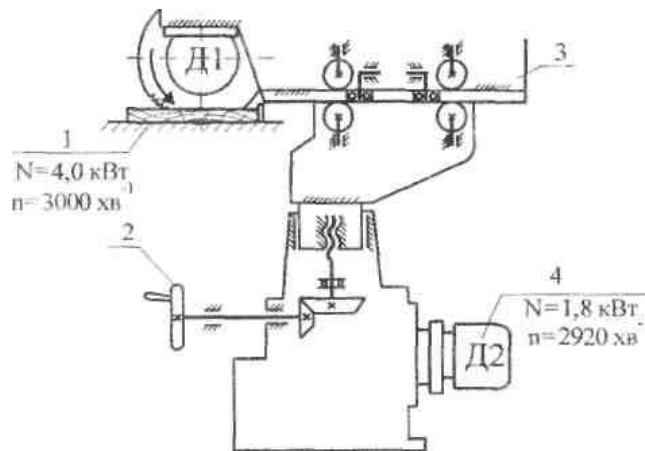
Кінематична схема верстата моделі ЦПА-40: 1 - механізм різання; 2 - маховичок; 3 - супорт; 4 - електродвигун гідропривода; 5 - гідроциліндр
